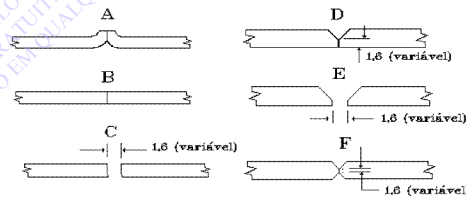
Tipos de Juntas para Soldagem TIG de Diferentes Materiais e Espessuras.
